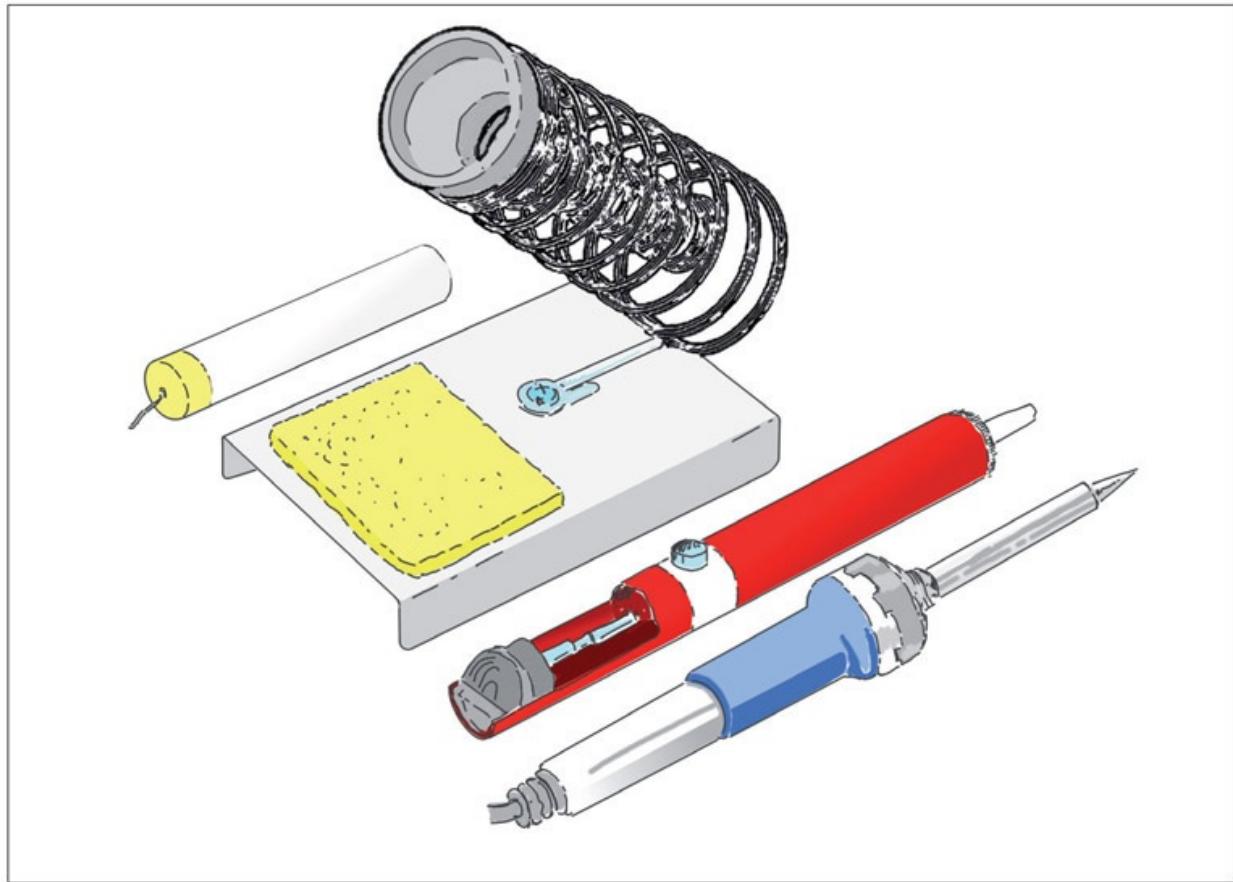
Herramientas para soldar: un soldador, una bomba para aspirar el estaño, un soporte de muelle para soldador con esponja para limpiar la punta y un carrete de estaño.
